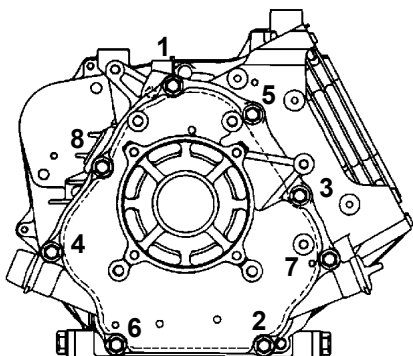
CS8.5-12. Sequenza di serraggio della piastra di chiusura.
